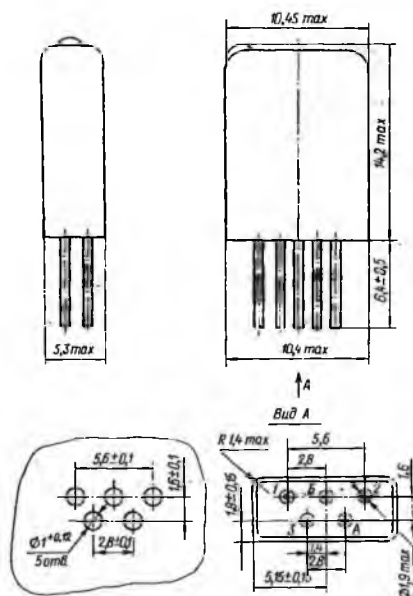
Конструктивные данные реле РЭК23, маркировка и разметка для крепления
